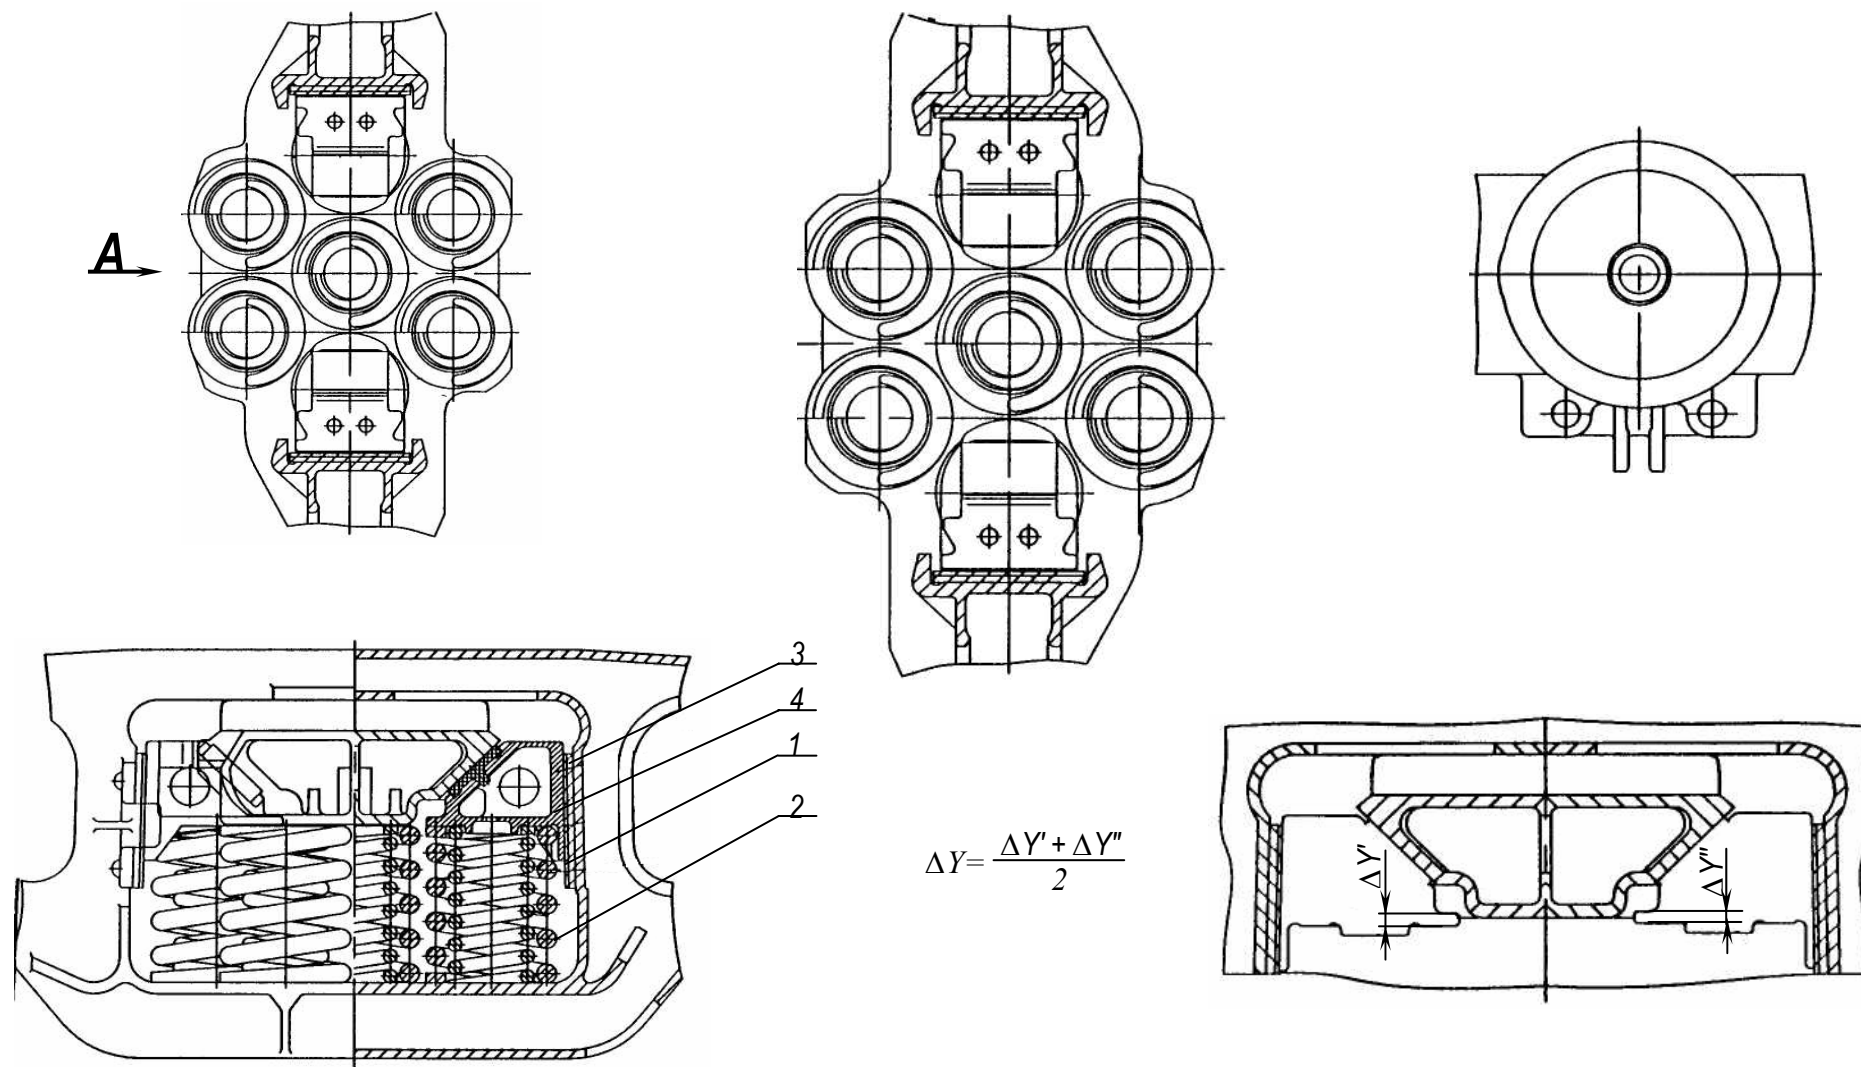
Рессорное подвешивание: 1 – пружина наружная; 2 – пружина внутренняя; 3 – фрикционный клин; 4 – планка контактная
